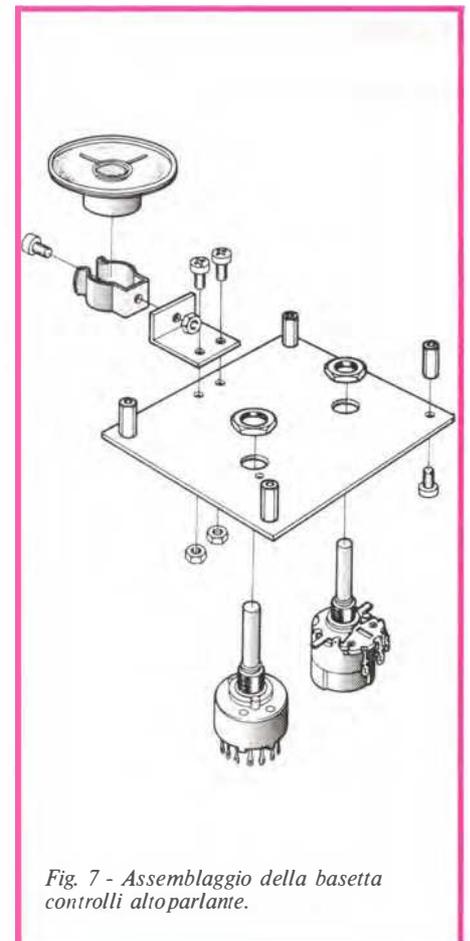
Assemblaggio della bassetta controlli altoparlante.
